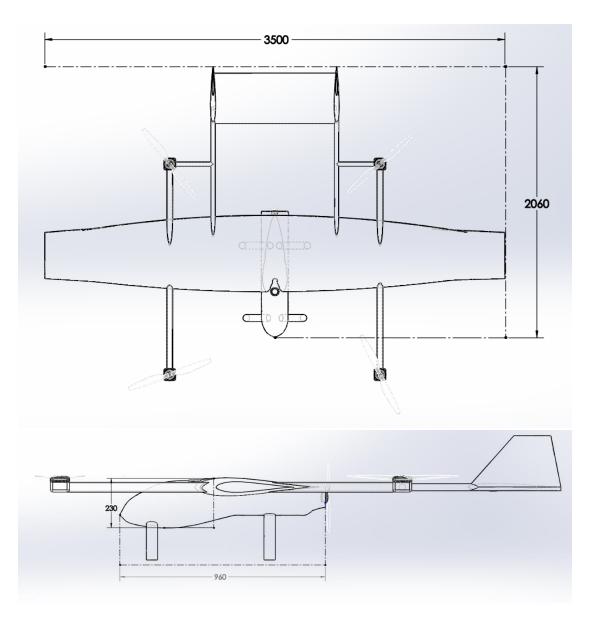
และ 9 รูปแบบ Drawing มุมมอง Top View และ Side View ตามลำดับ
